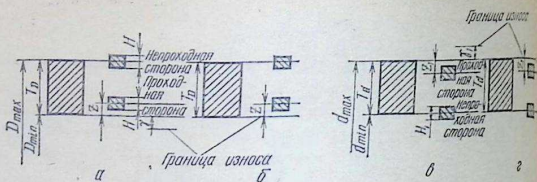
Схемы расположения полей допусков калибров:
